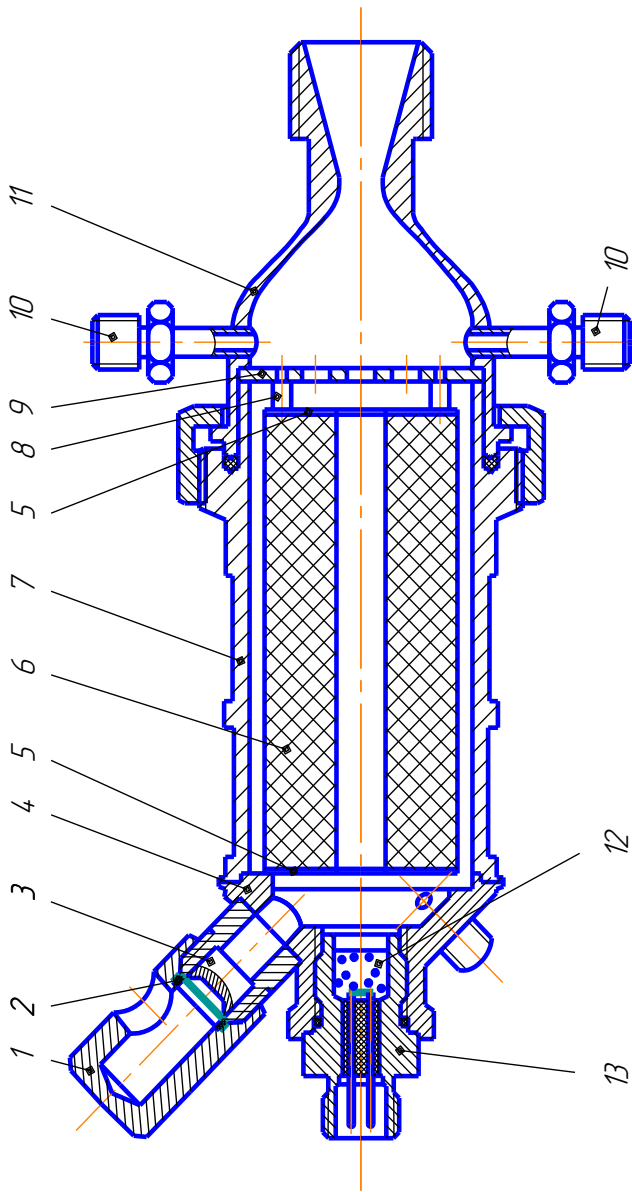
Экспериментальный ракетный двигатель твердого топлива:
